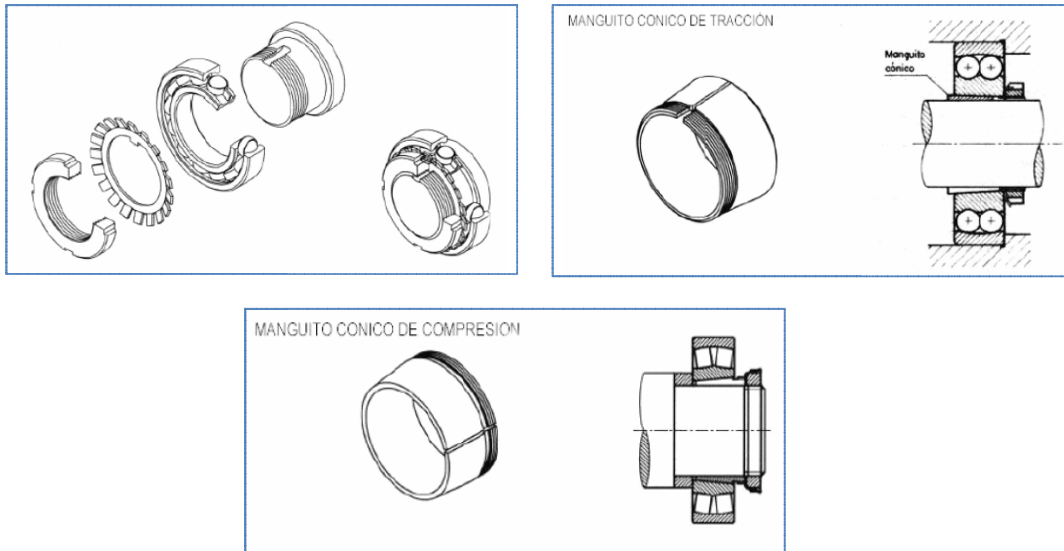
Técnicas de montaje y sujeción de rodamientos
